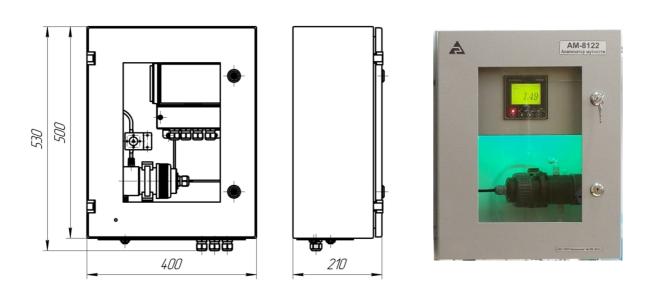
Шкаф монтажный ШГП-АМ.02 - габаритные размеры
